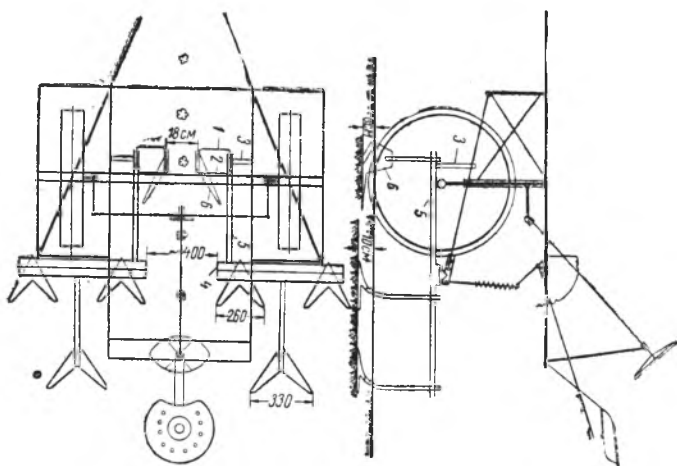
Схема секции лесного культиватора КЛТ-4,5Б с дополнительно установленными бритвами впереди бруса держателей:
